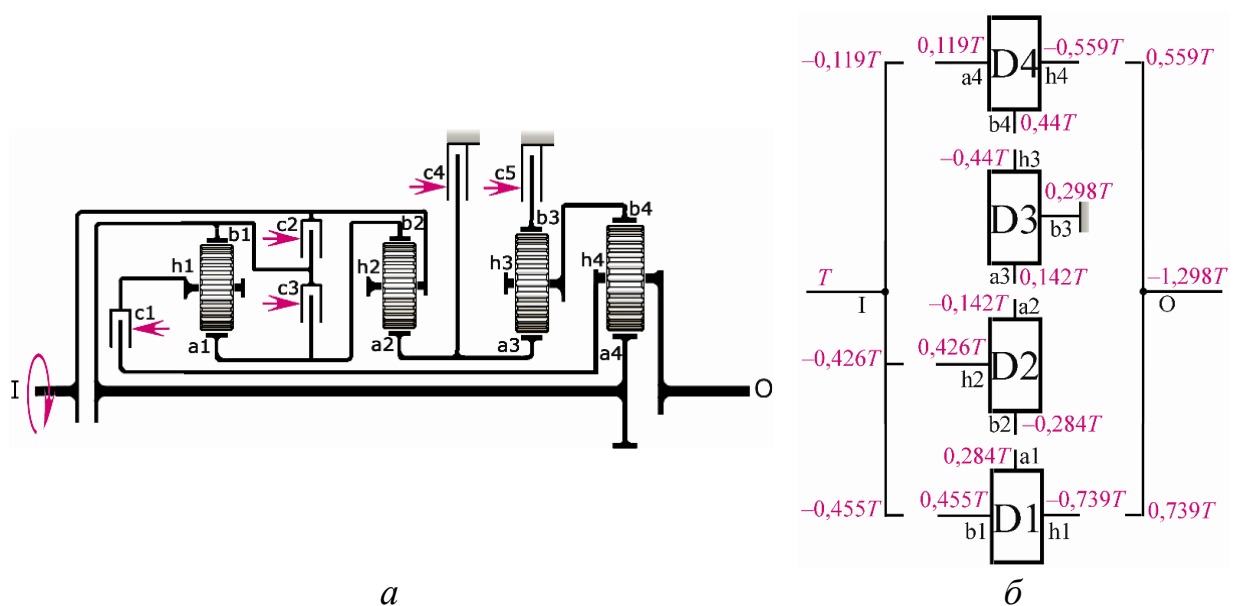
а – кинематическая схема 8-ми ступенчатой планетарной коробки передач; б – статический анализ 5-й ступени.
